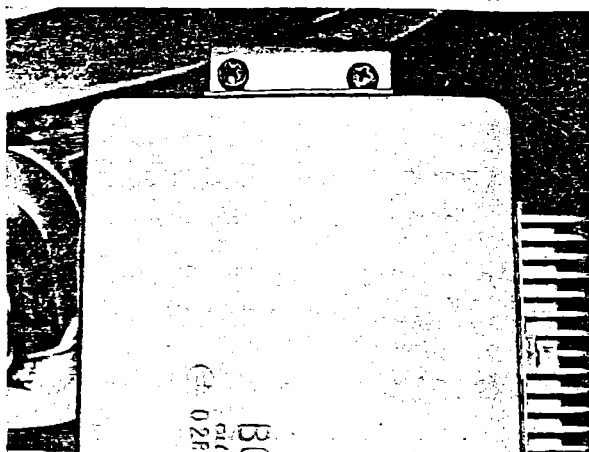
45 Befestigungsschrauben für Steuergerät, P 1800
